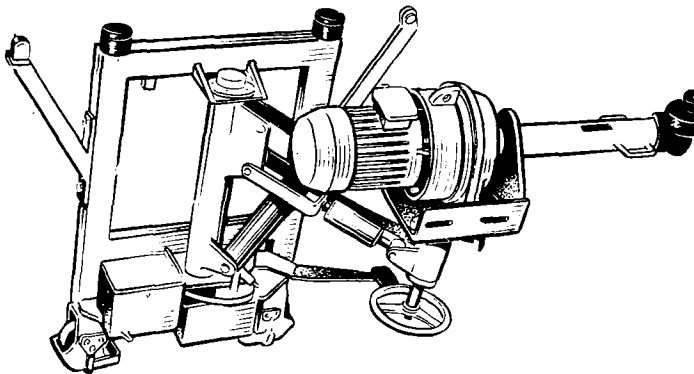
Гайковерт канавный модели И-314 для гаек стремянок рессор грузовых автомобилей
